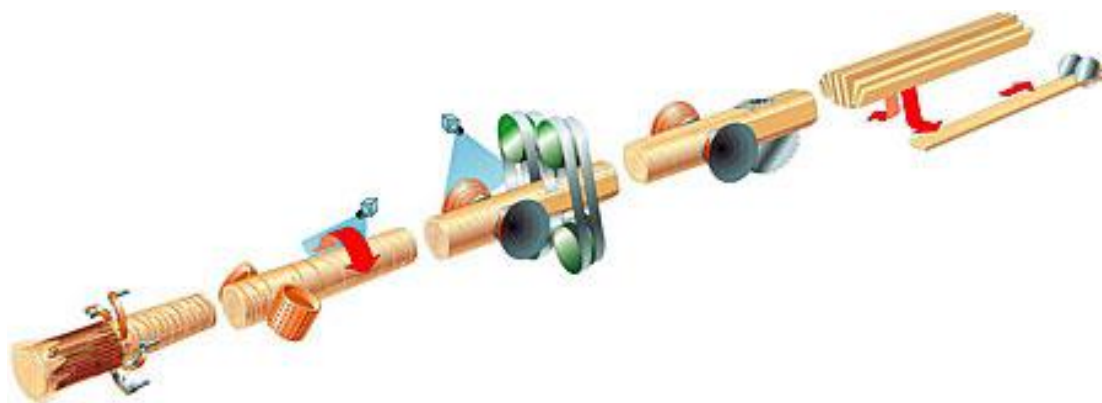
Схема фрезерно-ленточнопильного потока с использованием на втором проходе фрезерного узла и круглопильного делительного оборудования
